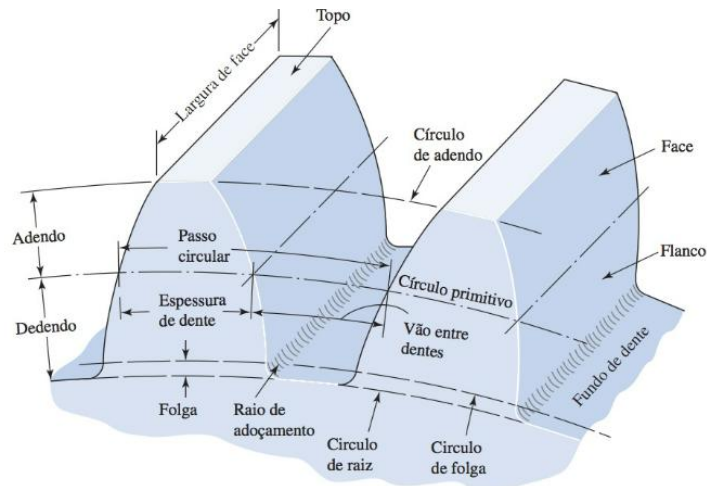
Nomenclatura para engrenagens cilíndricas de dentes retos, [6].
